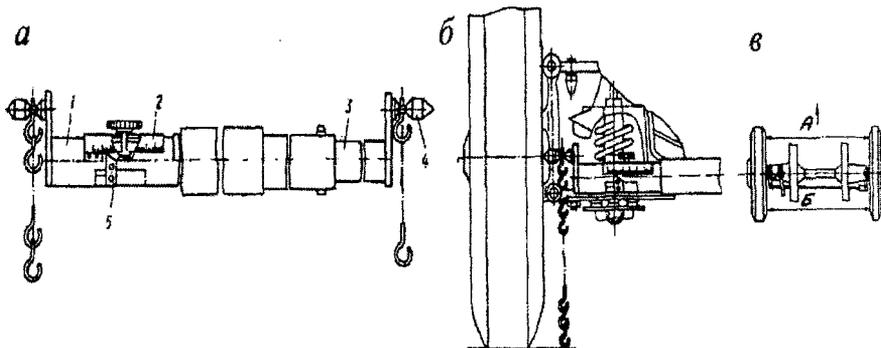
Линейка для проверки схождения передних колес мод. 2182: а – телескопическая линейка; б – установка линейки при замере; в – схема проверки схождения колес
